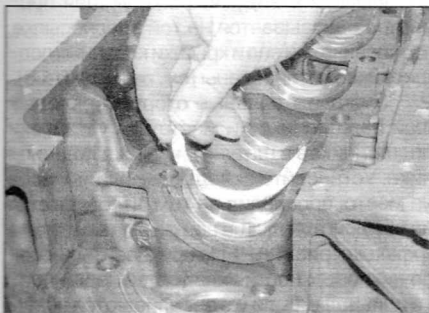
Установите верхние упорные шайбы на коренной подшипник № 2 таким образом, чтобы смазочная канавка была обращена наружу
